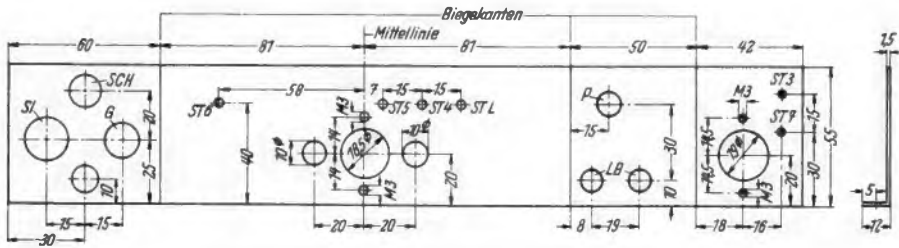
Winkelchassis W 2 für die Röhrenfassung
